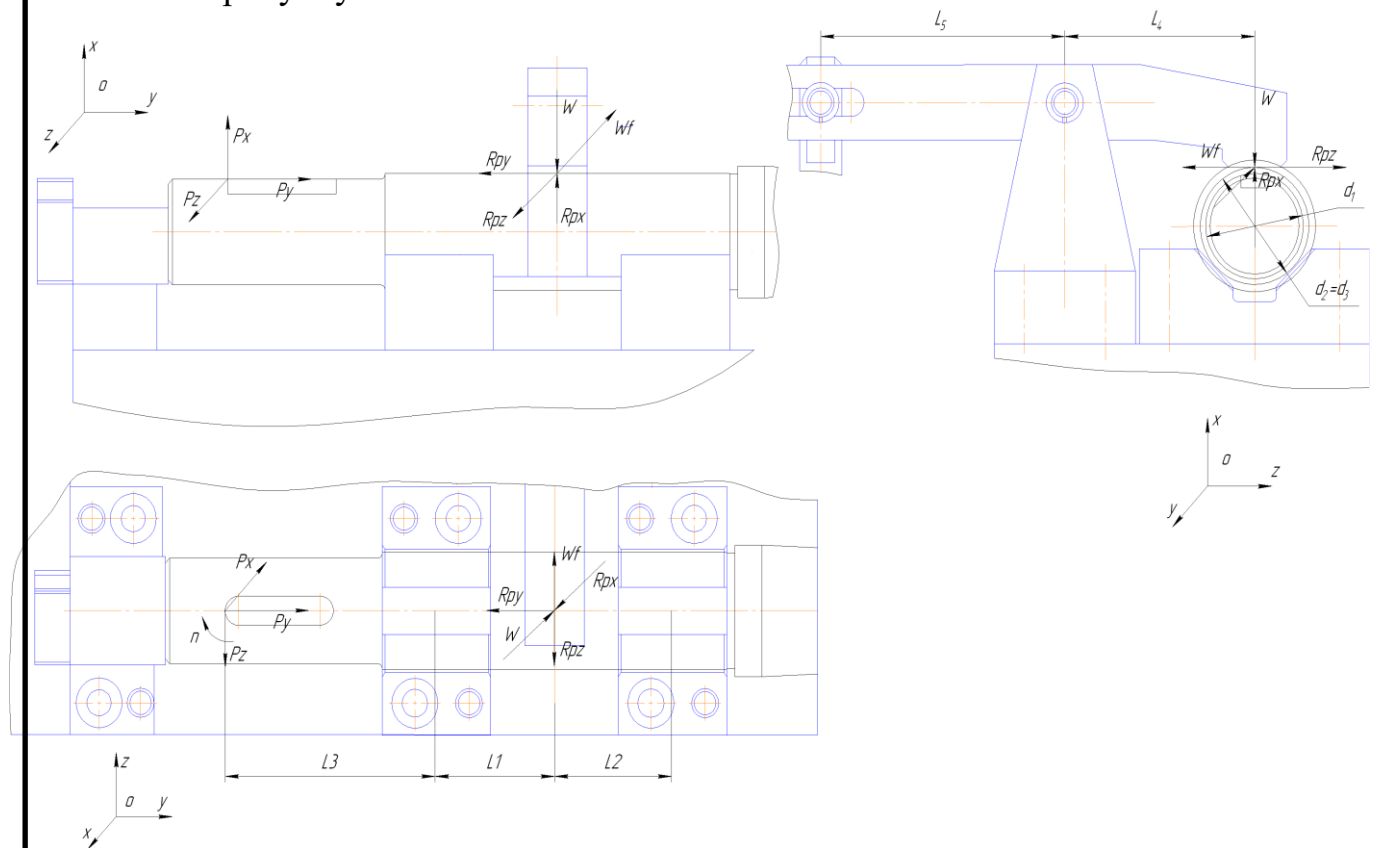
Розрахункова схема дії сил на деталь при фрезеруванні пазу 10N9_(-0,036)
